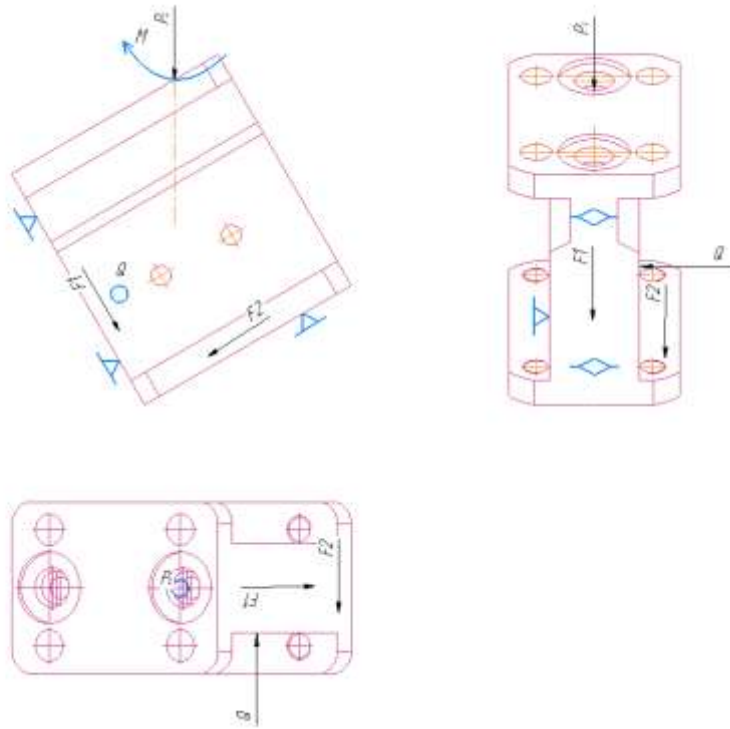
схема сил, действующих на заготовку и приспособление при сверлении
